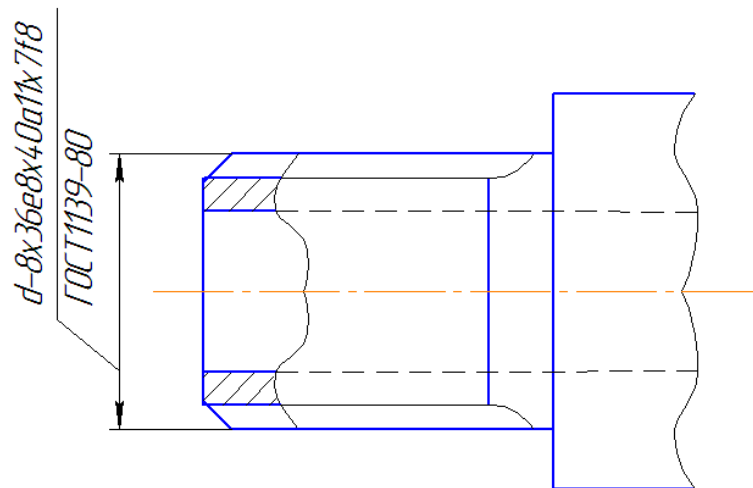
Обозначение шлицевого прямобочного вала.
